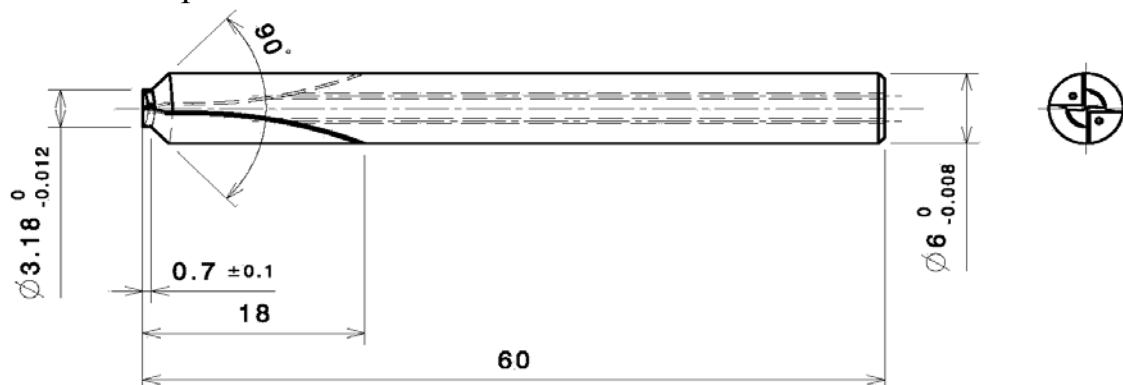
Чертеж твердосплавного сверла BOF D3.18X0.7X 60-6 из сплава UF10
